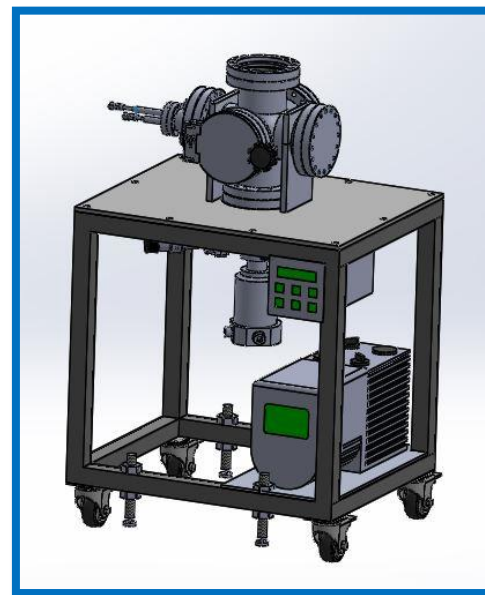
Ensamble general mostrando cada una de las posiciones de los componentes que conforman el equipo.
